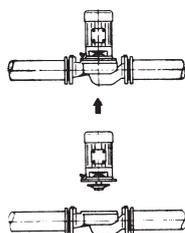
Vue du modèle IPL – Installation sur tuyauterie
